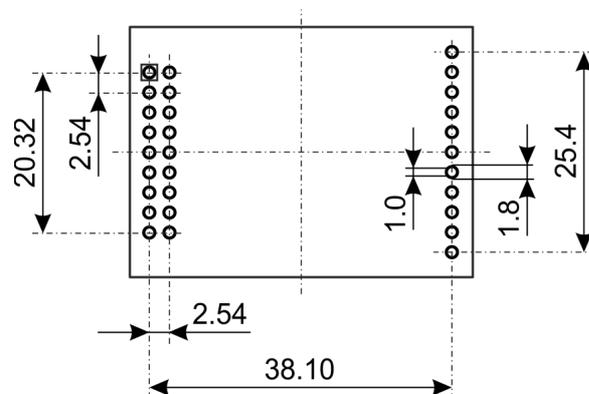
THT Footprint [mm] – Ansicht von oben
